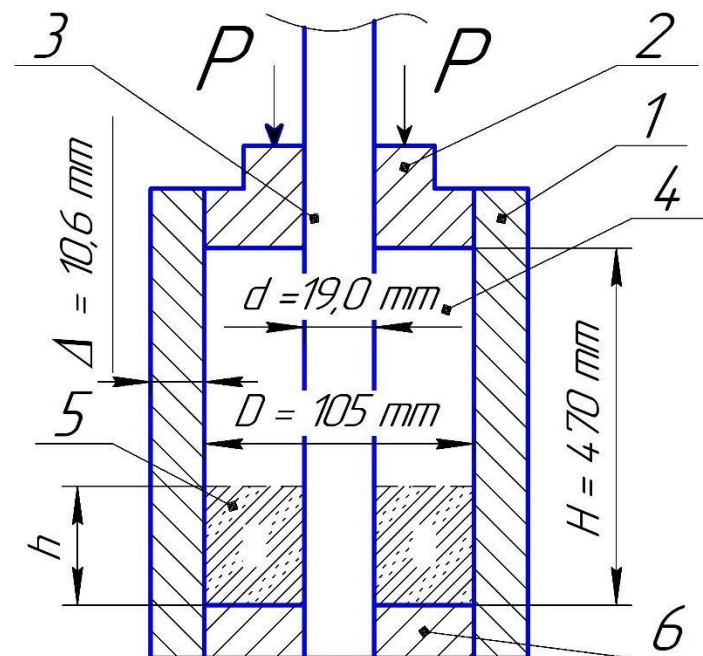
Схема компресійного пресування ПТФЕ-композитів: 1 – матриця; 2, 6 – верхній та нижній пуансони; 3 – дорн; 4 – навішування порошку; 5 – спресована таблетка [35].
